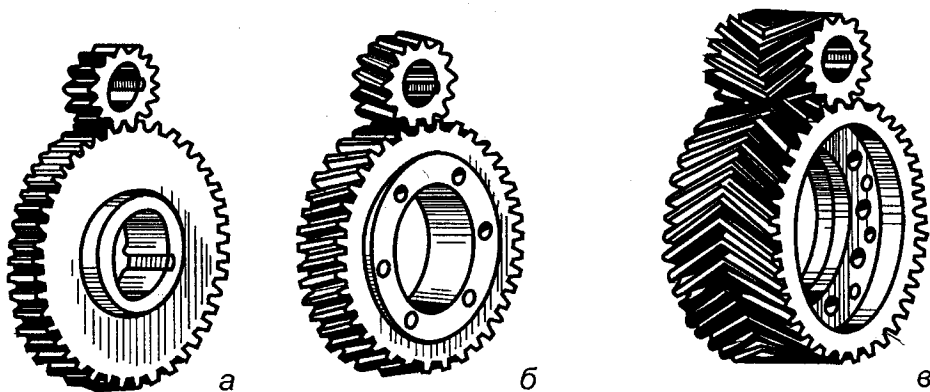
Передачі циліндричними зубчастими колесами між паралельними валами: а) прямозубі; б) косозубі; в) шевронні
